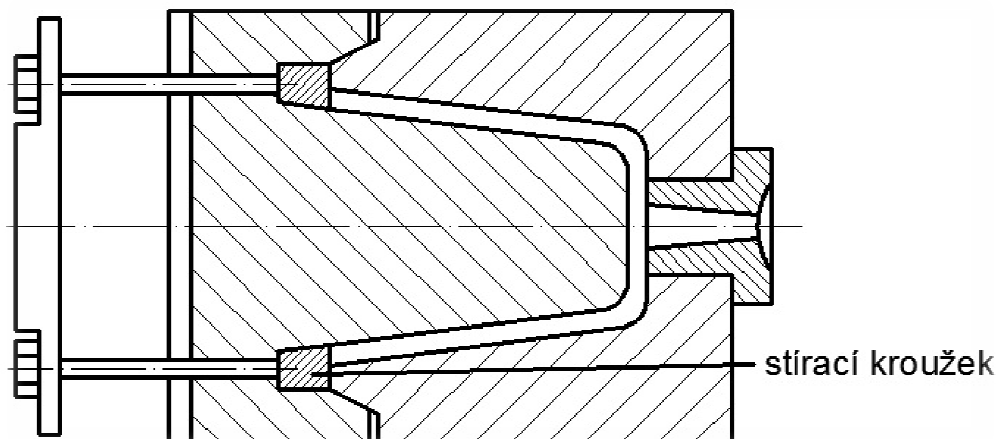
Odformování výrobku vyhazovacími kolíky [4]
